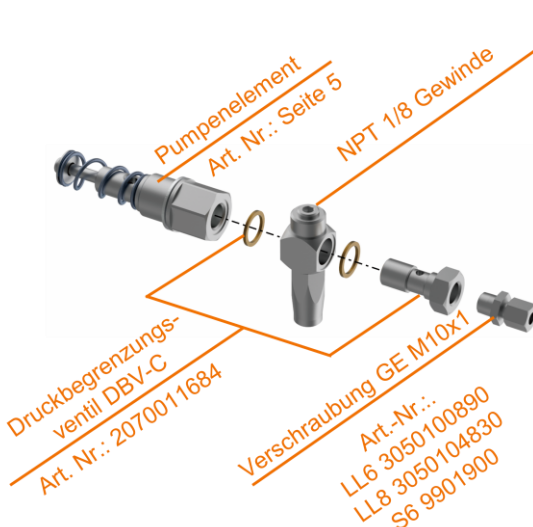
Explosionszeichnung PE mit DBV-C
